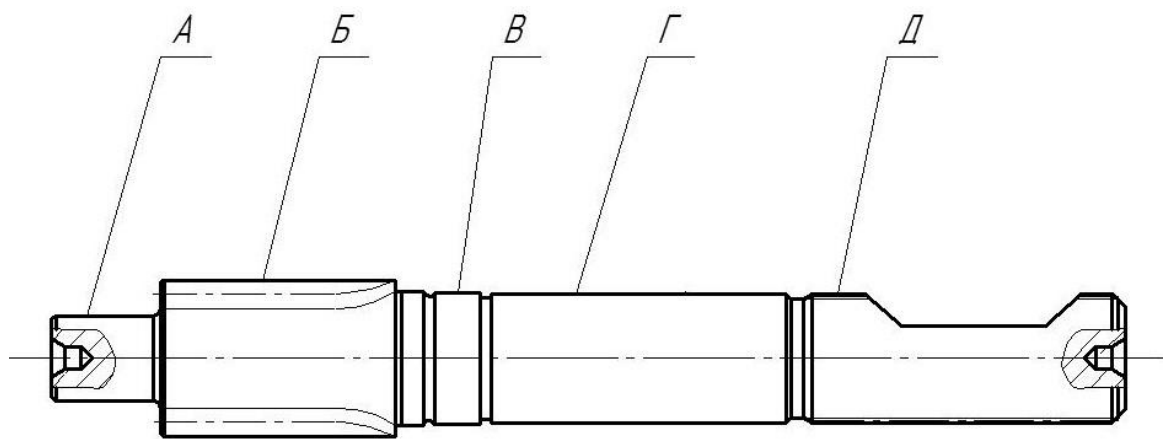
Відновлений вал-шестерня рульового механізму.
